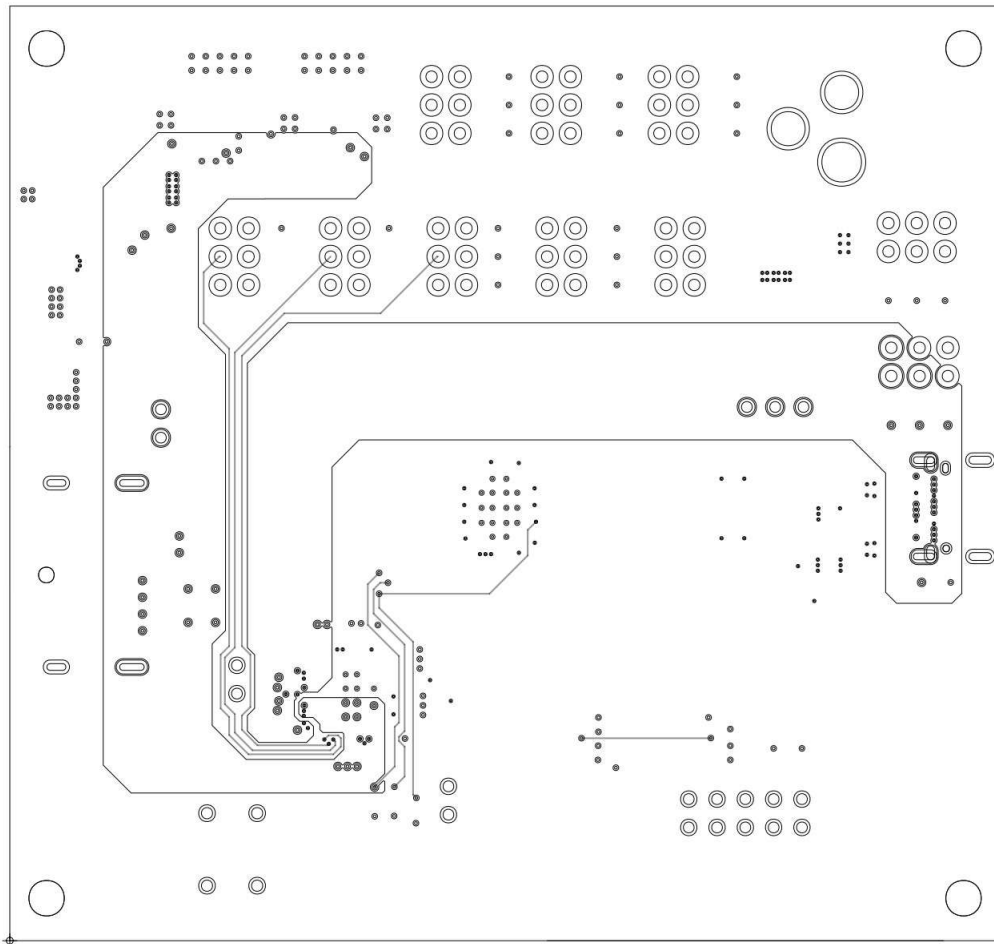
TUSB5461-Q1 EVM PCB 第 4 层 (信号)
